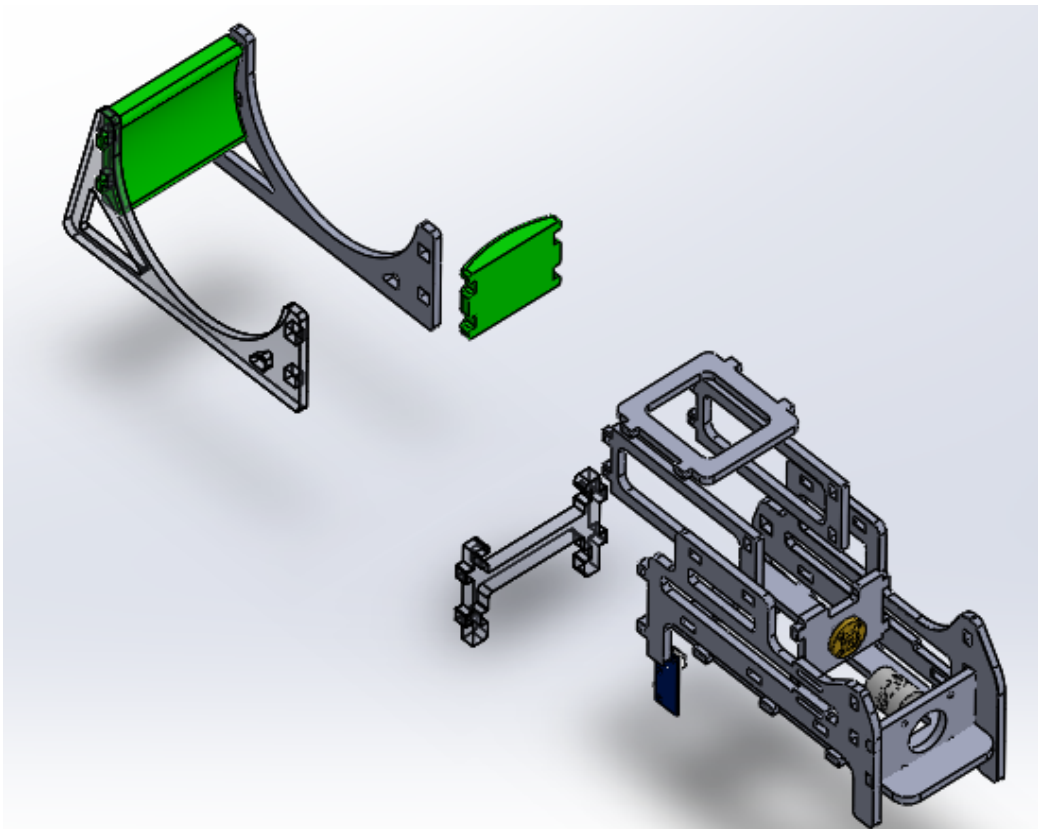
Vista explosionada del sistema mecánico en 3D del respirador artificial.
